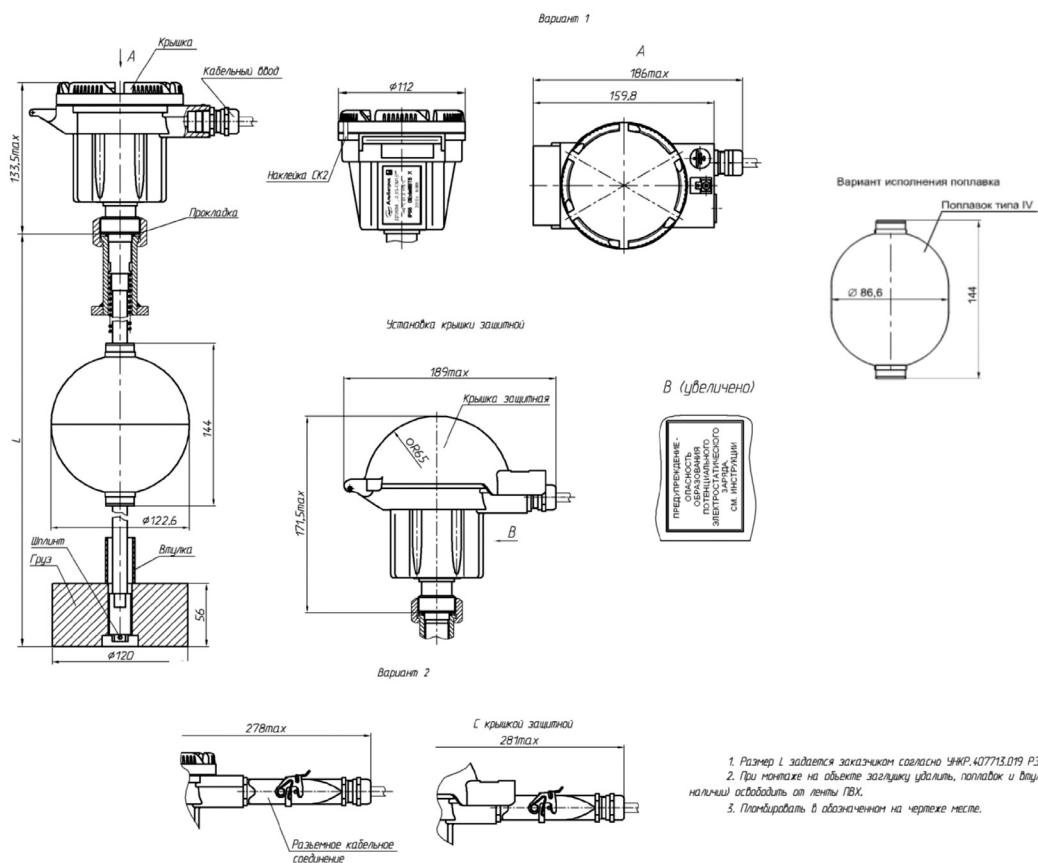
Габаритные размеры датчика ДПУ8М
